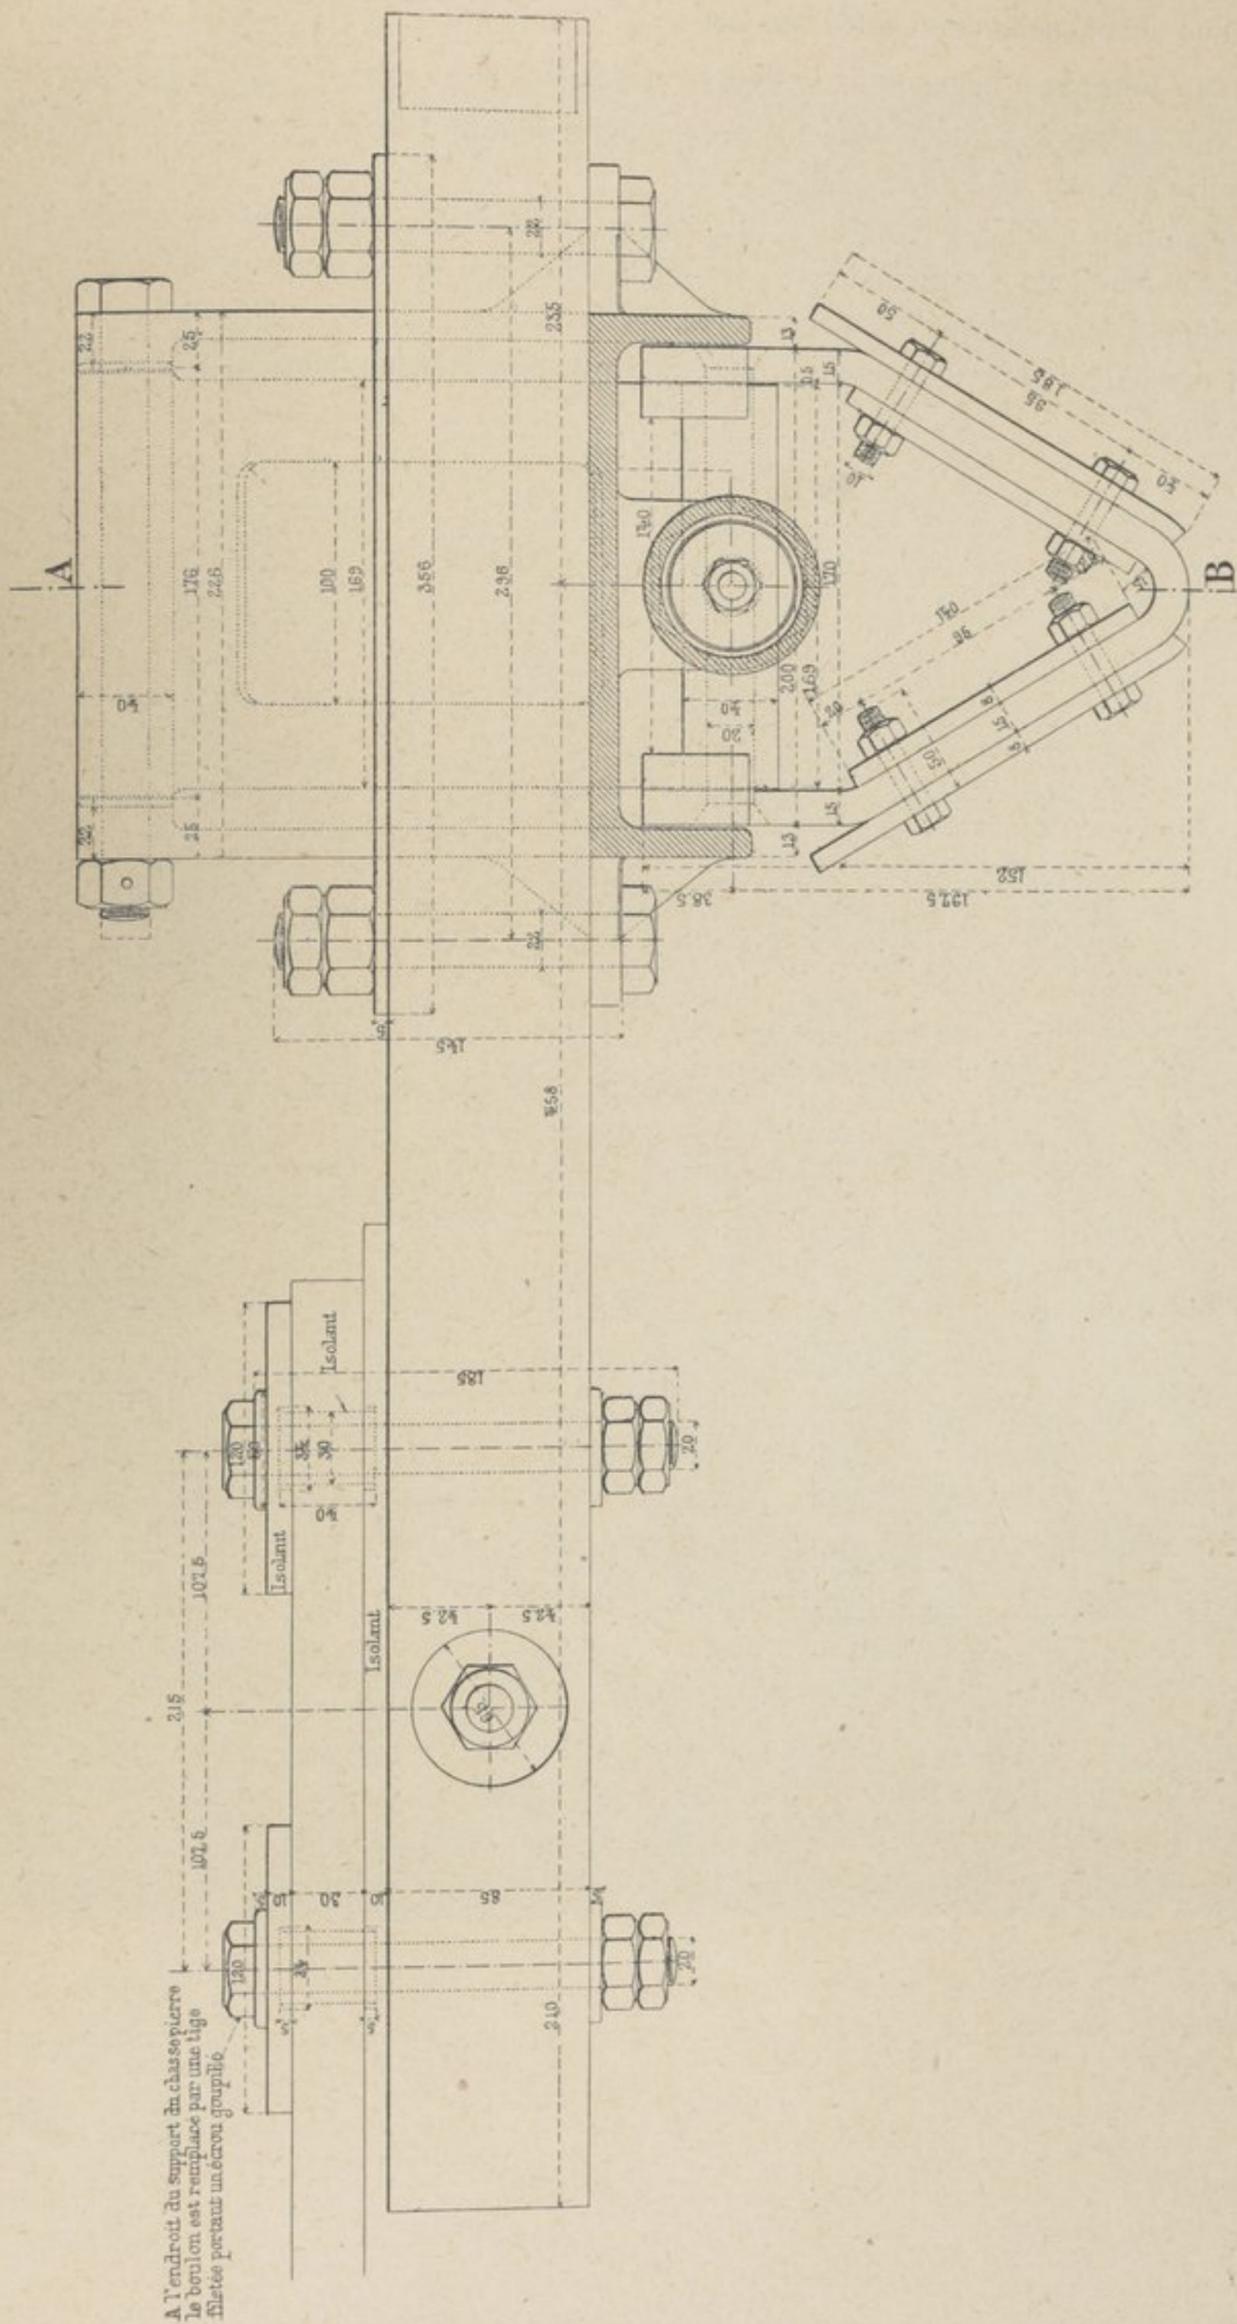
CHASSE-NEIGE AUTOMOTEUR (Vue de côté).
